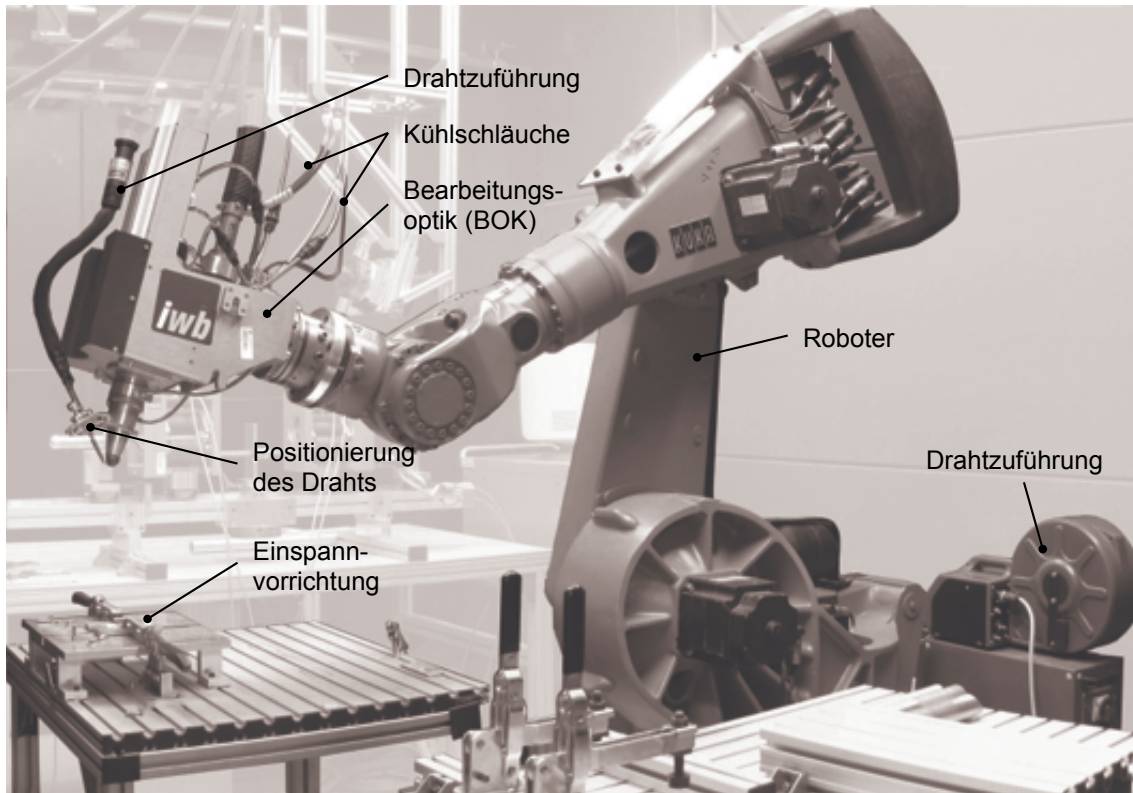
Versuchsaufbau für das BHLs mit Zusatzdrahtzuführung am Institut für Werkzeugmaschinen und Betriebswissenschaften (iwb) der TUM
